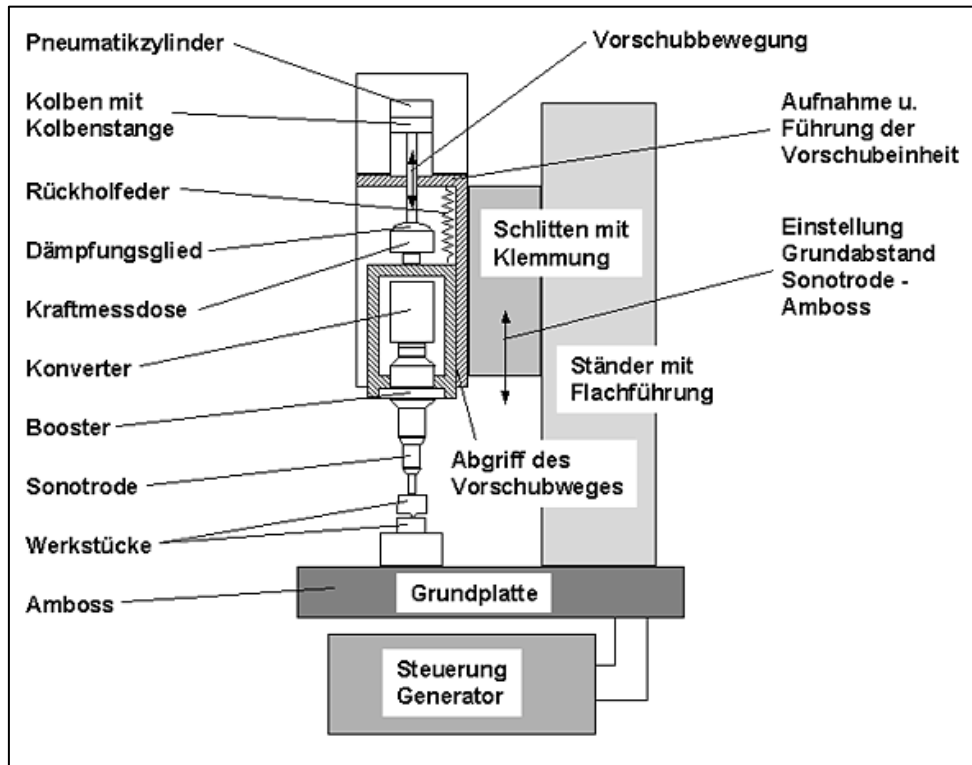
Aufbau einer Ultraschallschweißmaschine
